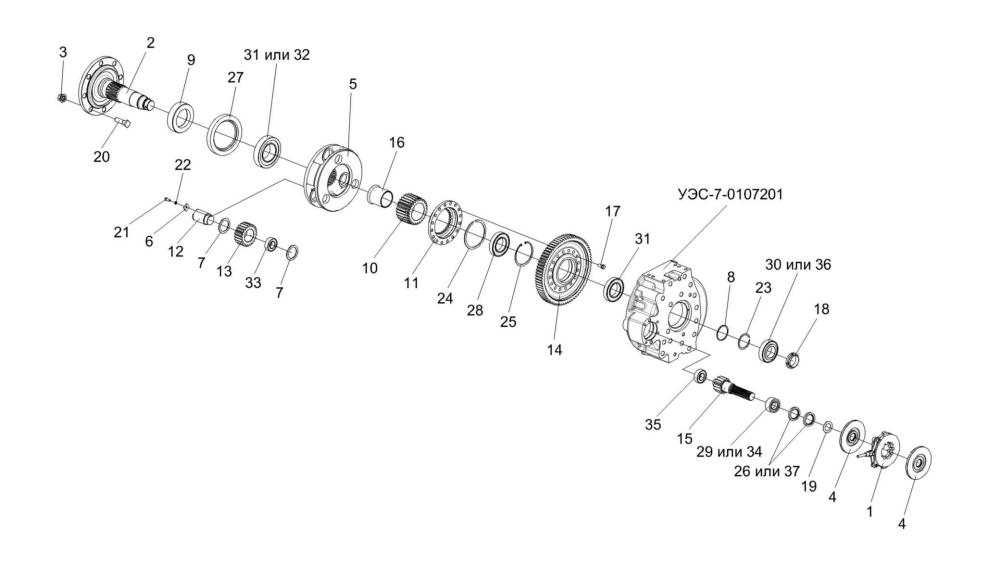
Редуктор левый МК-23М.03.000Ж-03 (валы, шестерни)
